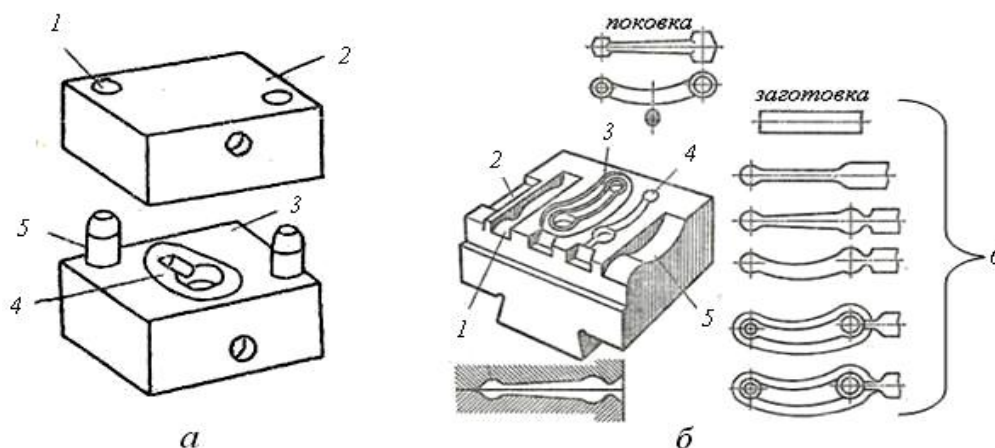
Штампи: а) – підкладний – однорівчаковий: 1 – направляючі отвори; 2 – верхня частина штампа; 3 – нижня частина; 4 – рівчак; 5 – штирі;
